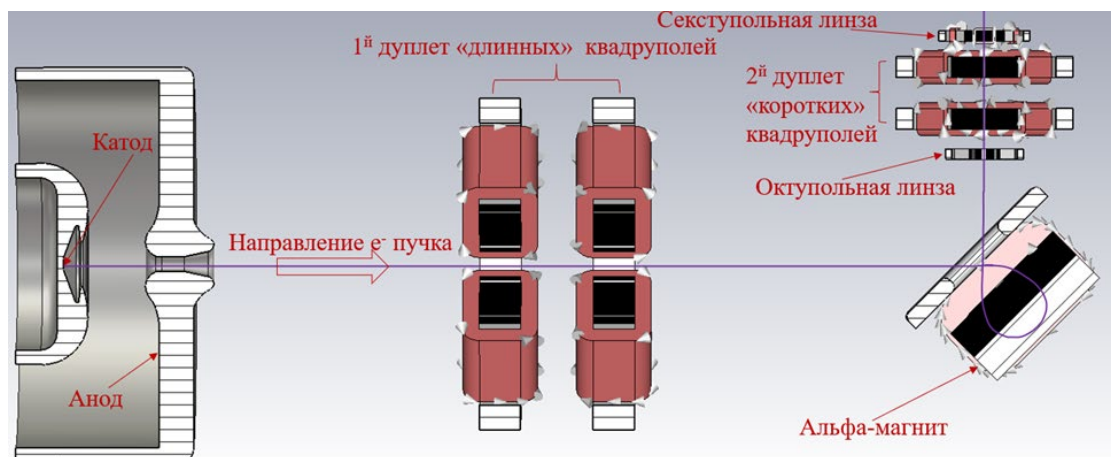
Схема расположения элементов разрабатываемой 120 кВ-й установки ЭЛС
